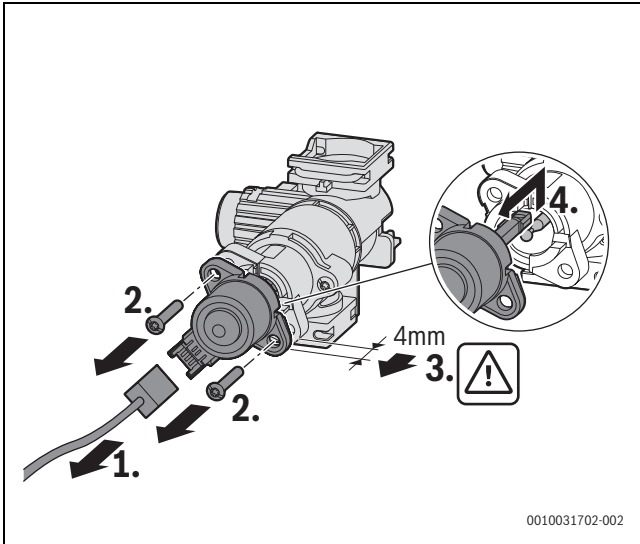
Motor am 3-Wege-Ventil ausbauen (Variante mit Schrauben)
